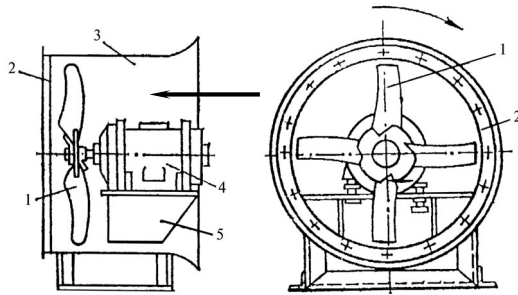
Схема вісьового вентилятора: 1 - робоче колесо; 2 - фланці (для приєднання повітропроводу, або для закріплення вентилятора на опорі); 3 - циліндричний корпус (кожух, обичайка); 4 - електродвигун; 5 - опора.
